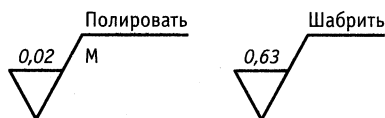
Пример приведения вида обработки в обозначении знака шероховатости поверхности
